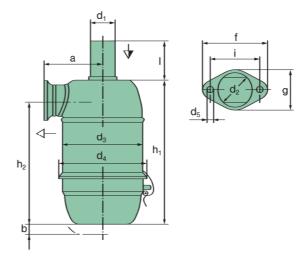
Ansaugstutzen glatt; Befestigung durch Flansch am Reinluftstutzen
